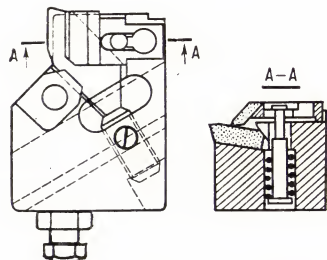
Резец конструкции ВНИИ с твердосплавной пластинкой.
